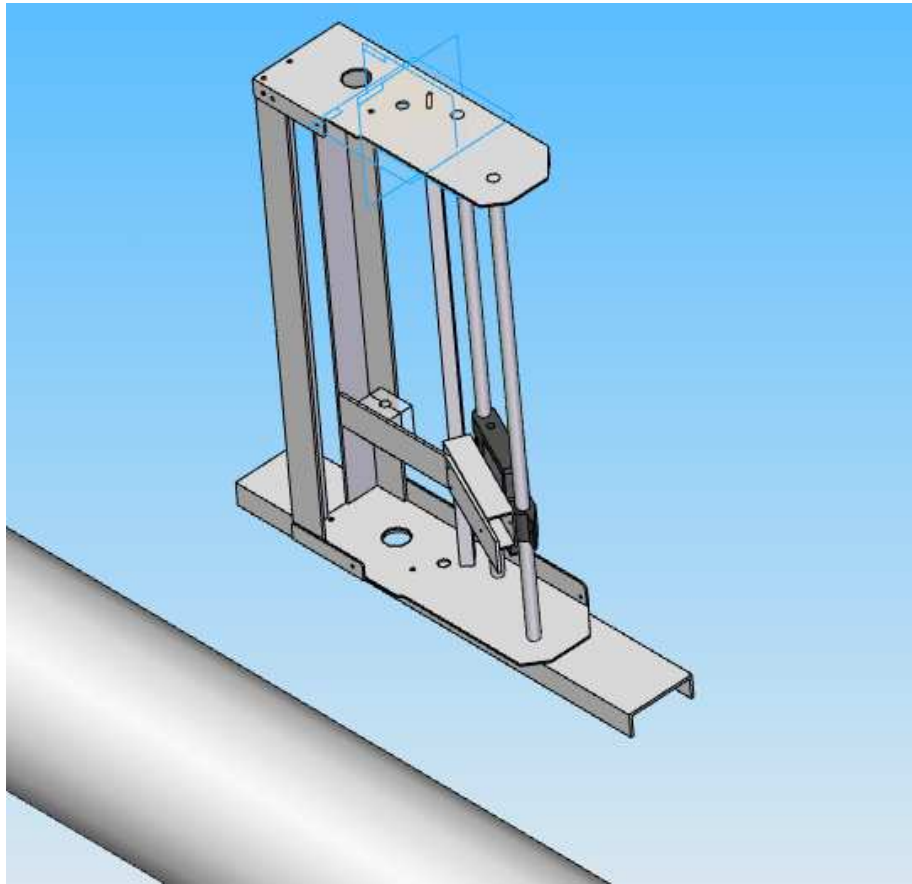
Croqui da vista isométrica do conjunto fixador e elevatório da haste do sensor prestes a ser montado.
